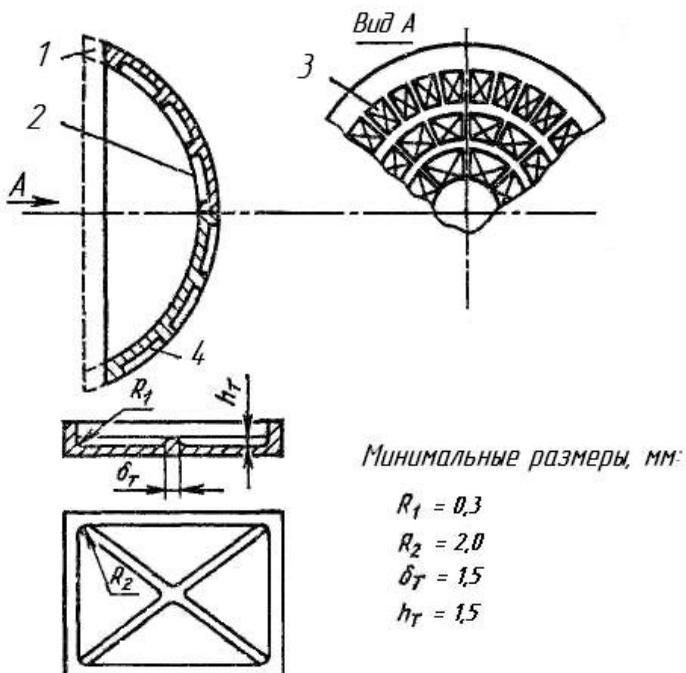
Мало жесткие корпусные детали с оребрением и тонкой стенкой
